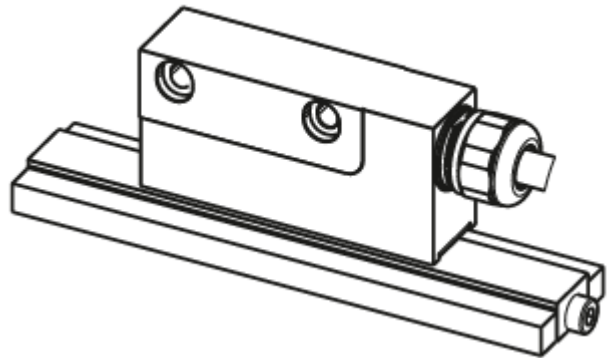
Montagebeispiel - Magnetband, stirnseitig verschraubt
